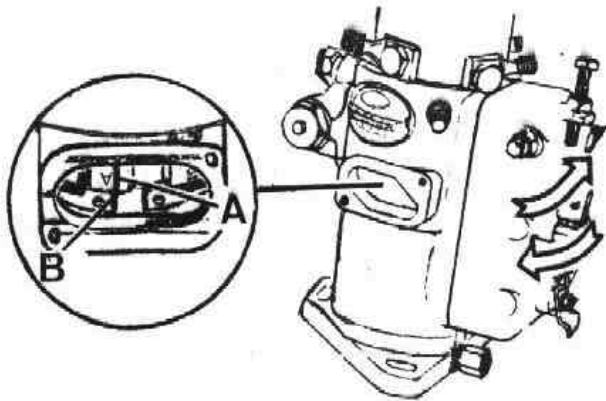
Ajuste de la bomba una vez montada en el motor
